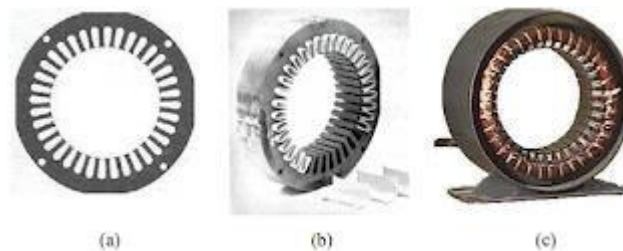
Penampang Stator dan Rotor Motor Induksi Tiga Fasa
